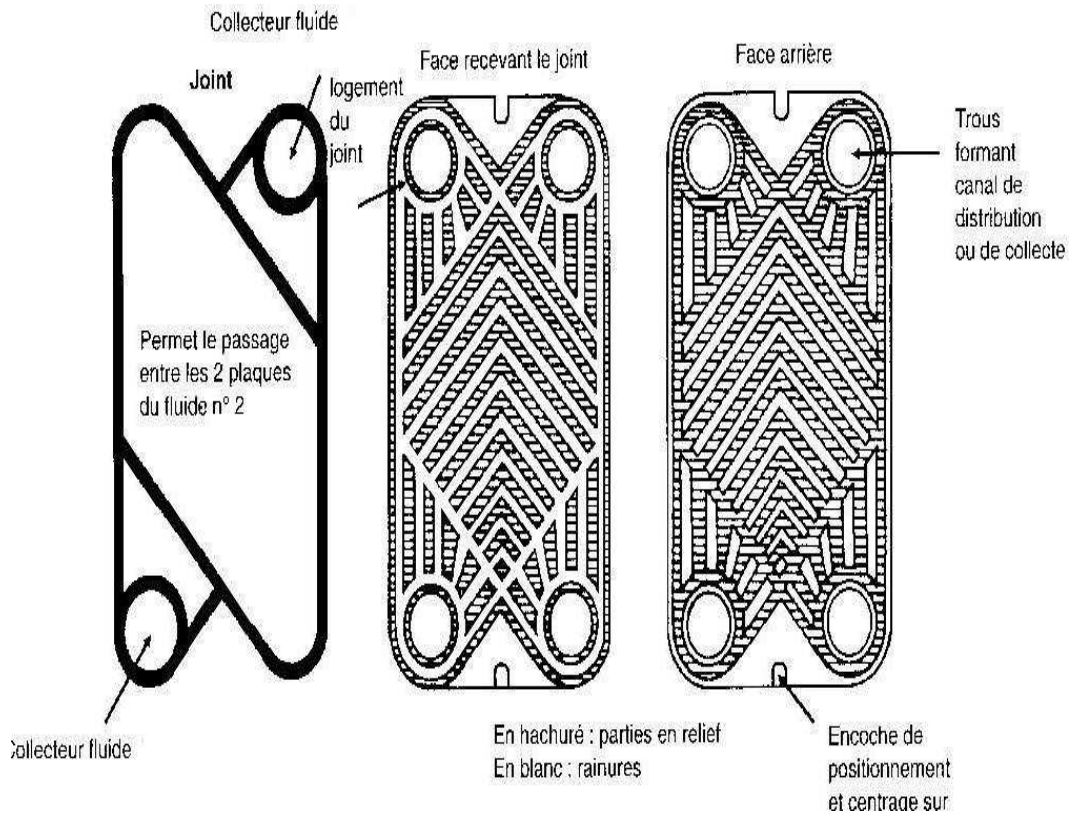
Détail d'une plaque avec joint d'étanchéité.
